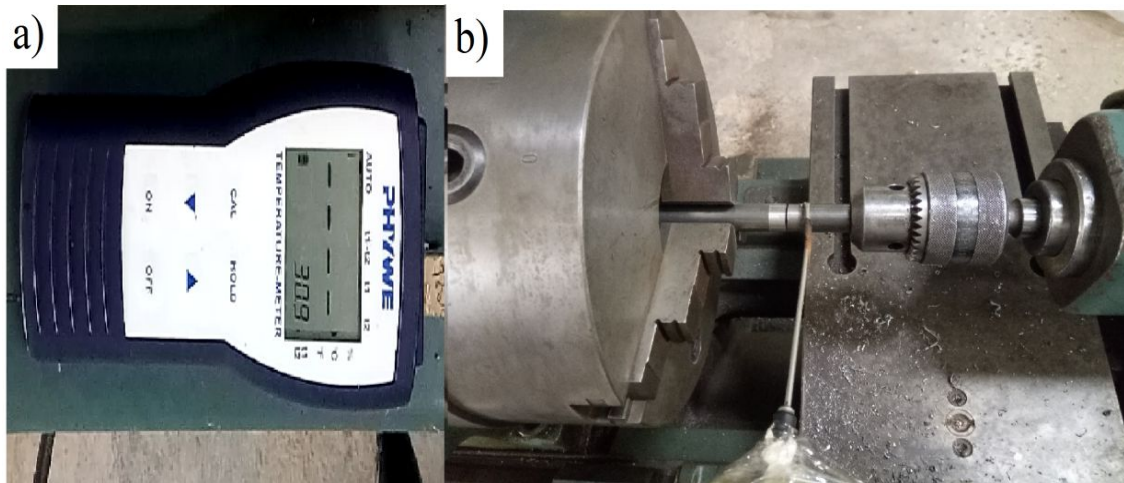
photographie du dispositif. a) Thermocouple. b) Installation de thermocouple sur la pièce fixe.
